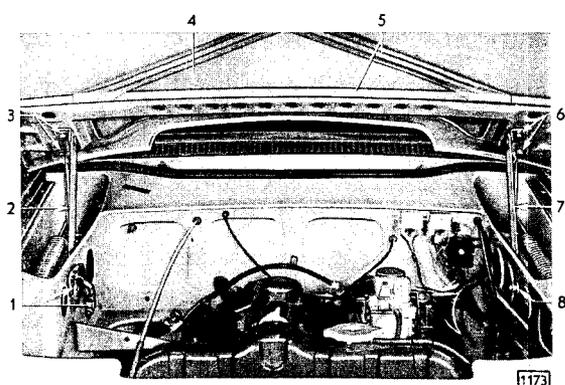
Befestigung der Motorhaube an Haubenscharnieren
